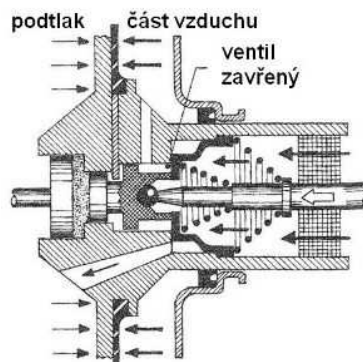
Podtlakový posilovač brzdného účinku v klidovém stavu [5]
